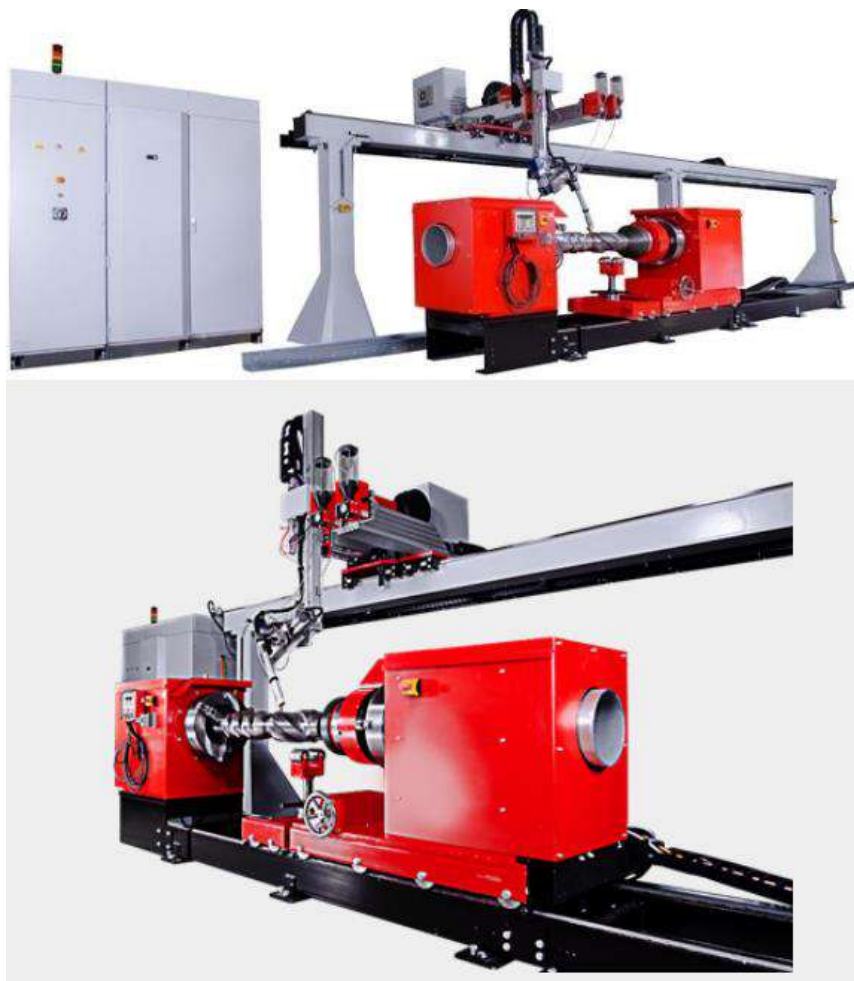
Установка для наплавлення бурових труб [23]
